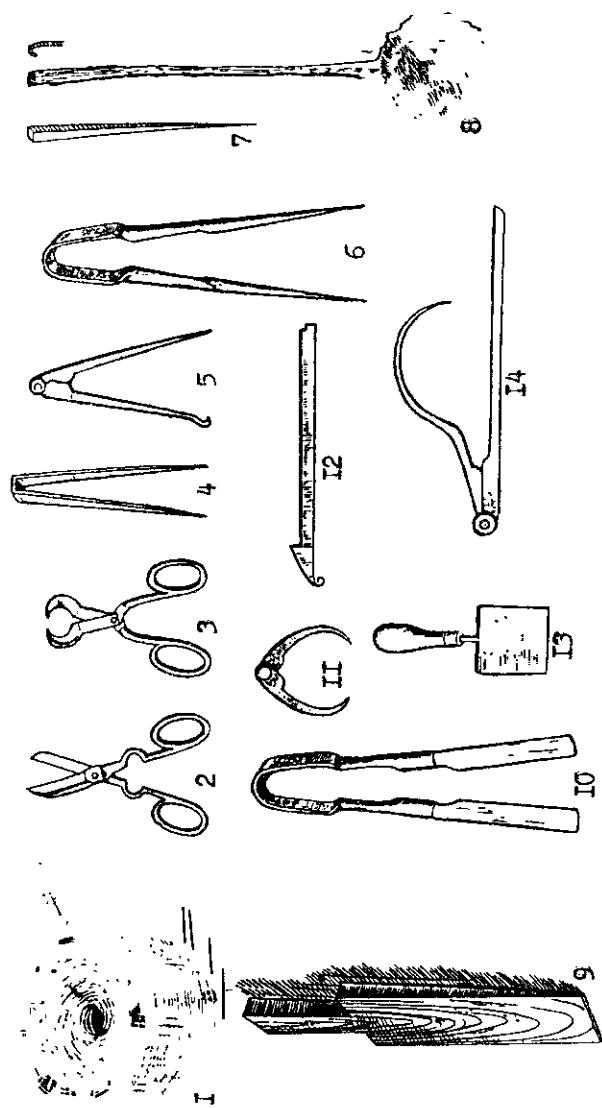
Рабочие инструменты стеклоделов (1.9. - по М. А. Безбородову; 2-8 и 10-14 — по Ю. Л. Щаповой); 1 — деревянный ковшик для розлива стекломассы; 8 — бронзовый ковш для розлива стекла из поселения у с. Комарово; 2-3 — ножницы для разрезки стекла; 4-6, 11, 14 — циркули и кронциркули для разметки стекла; 9, 13 — гладилки; 12 — отшибалка; 7 — стержень для разметки.
